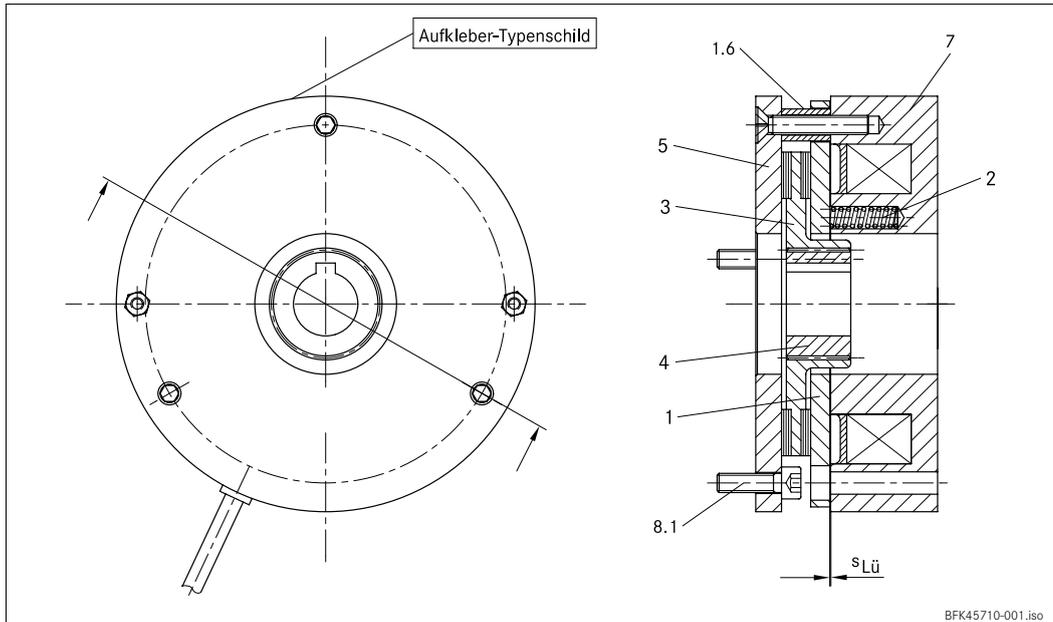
Aufbau der Federkraftbremse BFK457-01...16 Compact, komplett montiert mit Rotor und Flansch
